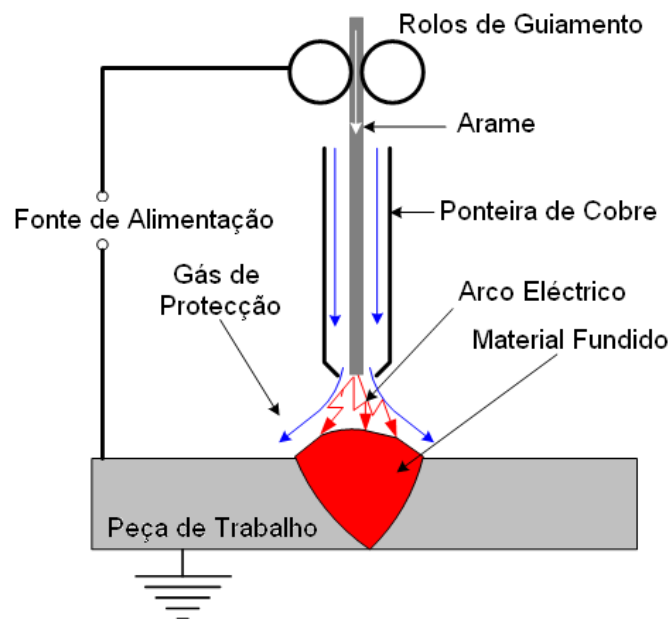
Processo de soldadura MIG/MAG [3].
